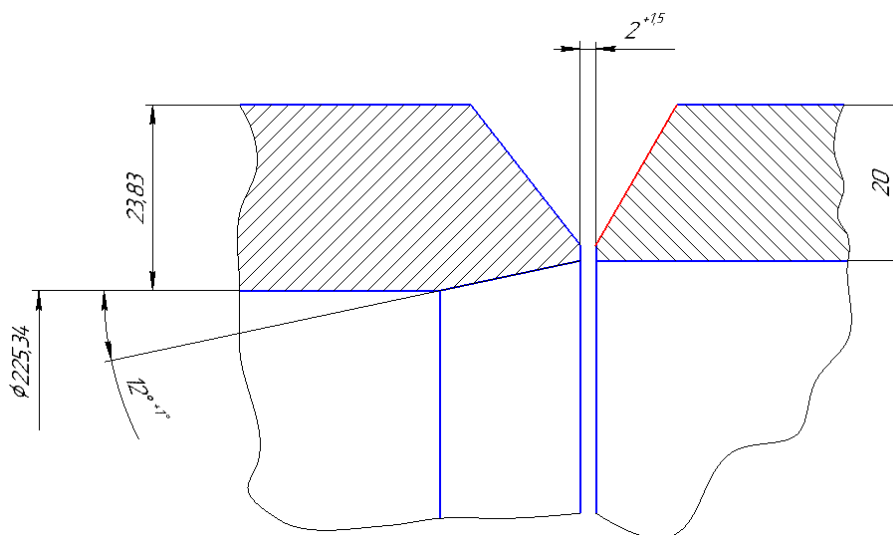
Сборка элементов паропровода под сварку
